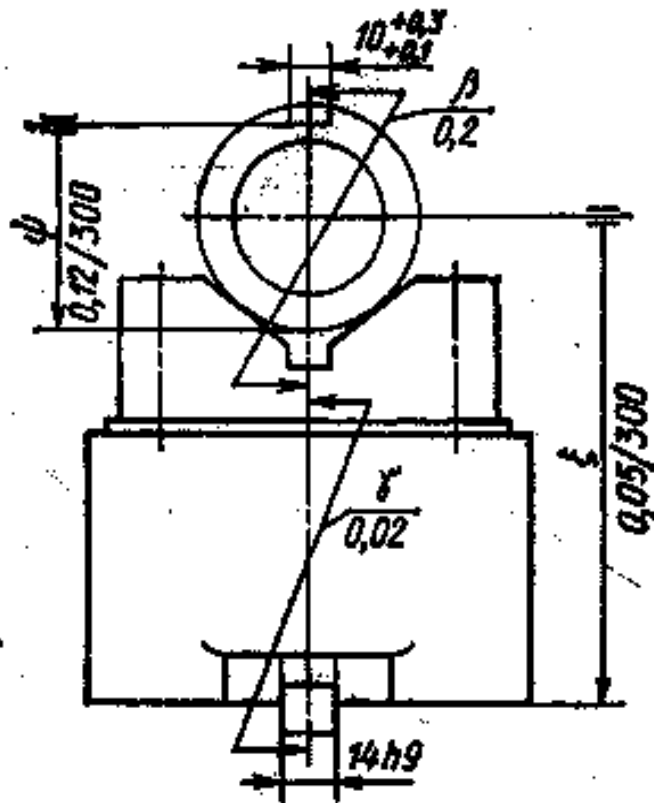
Принципиальная конструктивная схема приспособления для фрезерования паза
